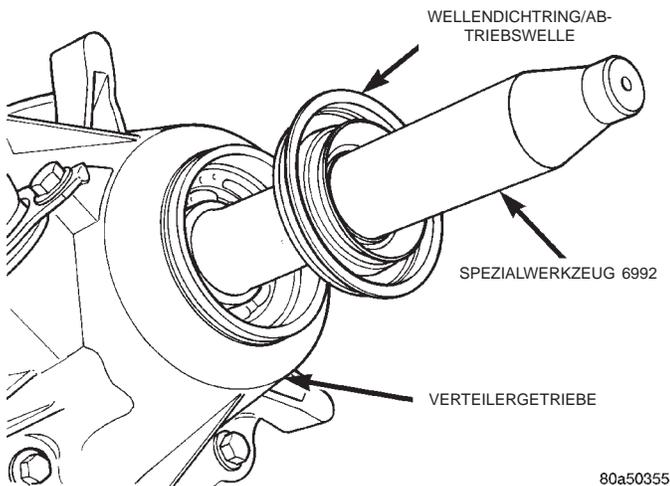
Dichtring der Abtriebswelle und Spezialwerkzeug
